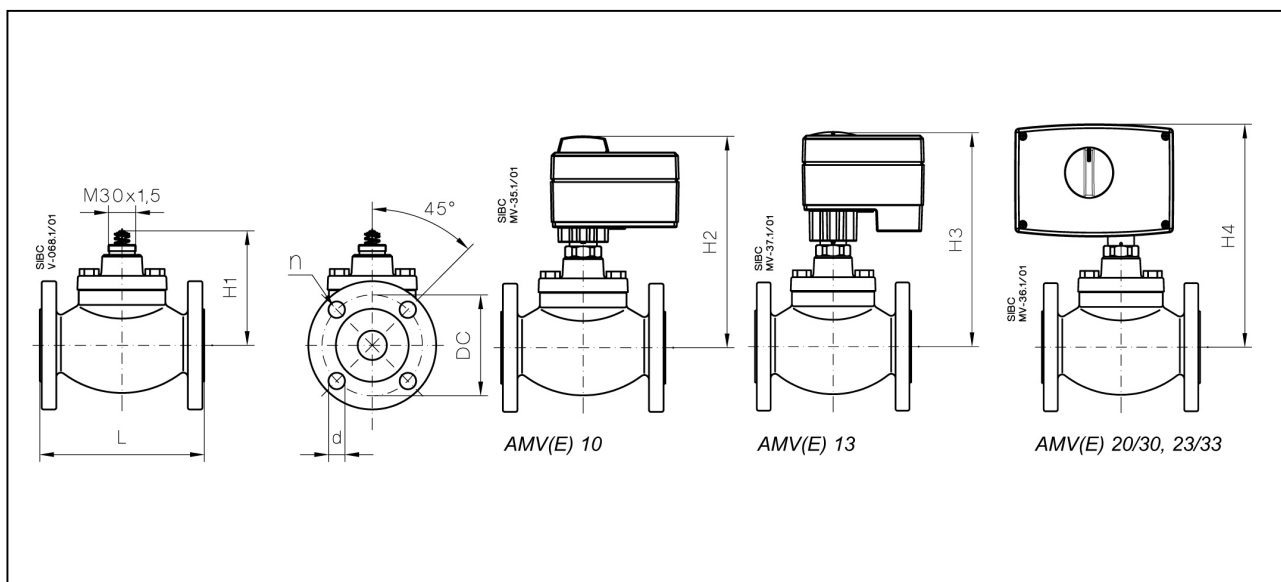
Габаритные присоединительные размеры клапанов VB2
